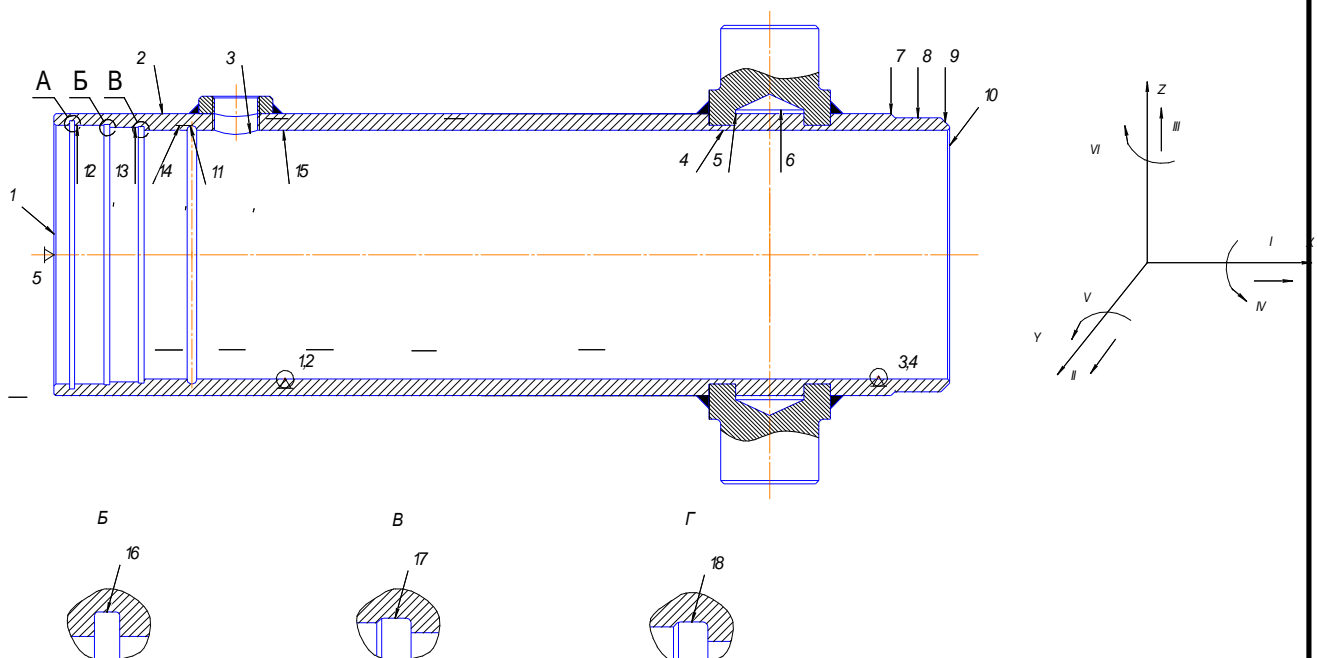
Основні поверхні корпусу 503А-8603510-03
